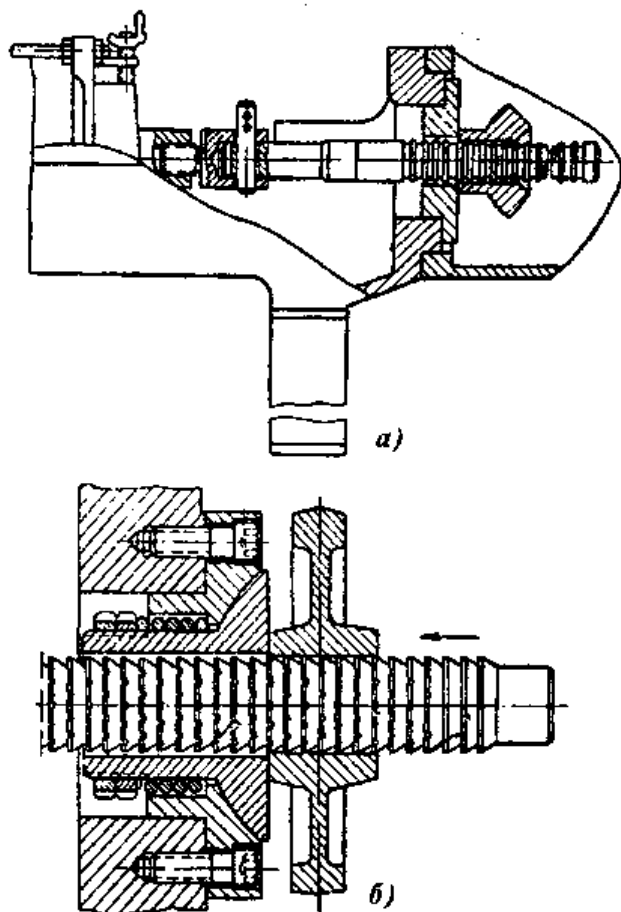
Схеми встановлювання деталей на протяжних верстатах
